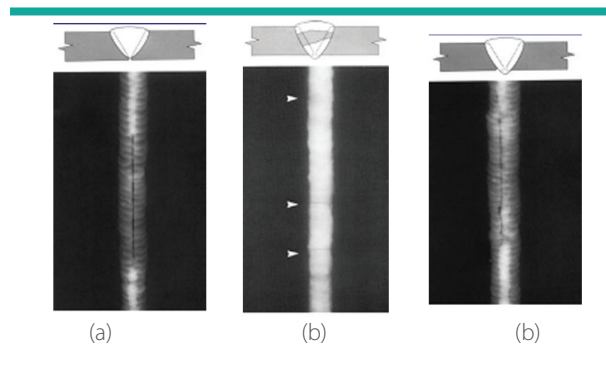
(a) Falta de penetración. (b) Fisuras transversales. (c) Socavación de raíz.
